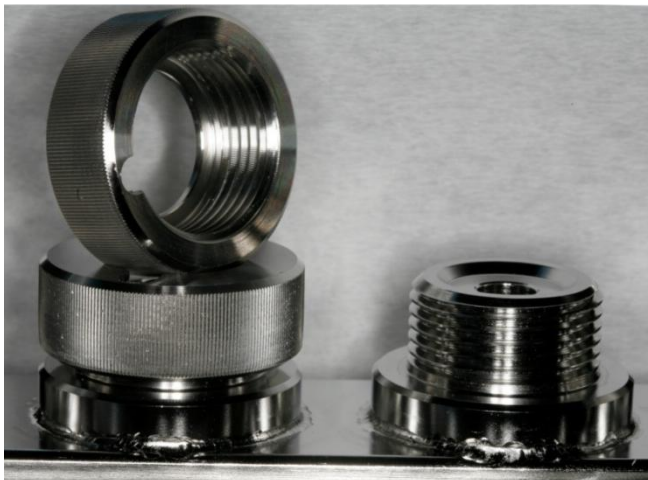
Aufnahme-Unterteil mit Gewindebuchse (rechts) auf der Leiste eingeschweißt und abgeschraubtem Aufnahme-Oberteil auf einem kompletten Aufnahmeteil (links) im RDG4.
